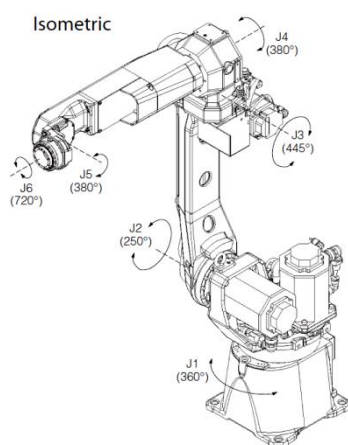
Робот для сварки ARC Mate 100iC
